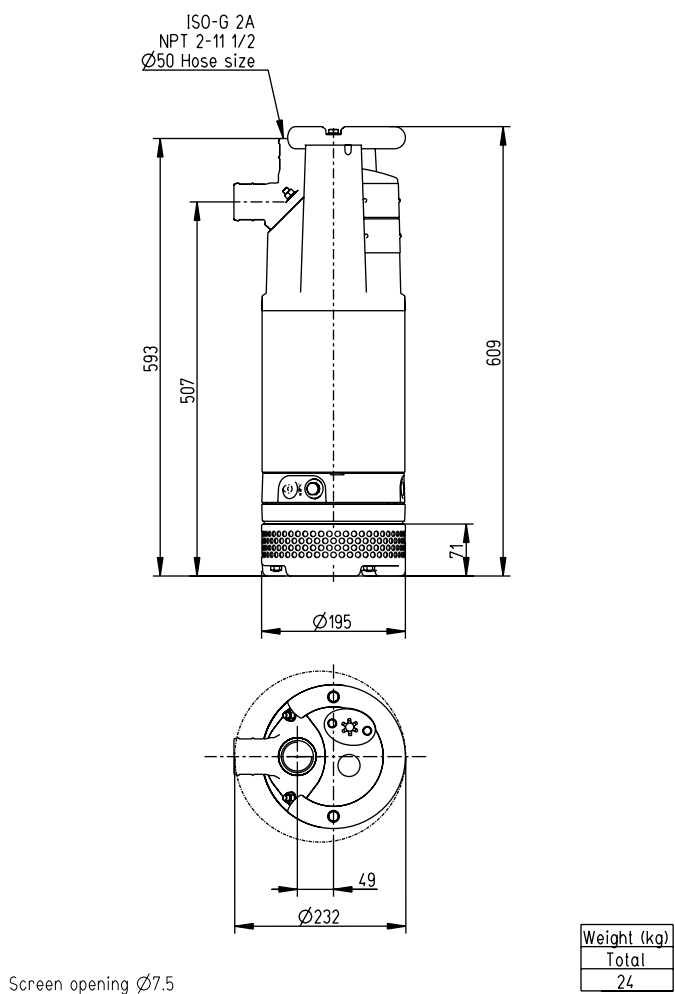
Стандартное исполнение, двигатель в сборе, 13-10-2BB
